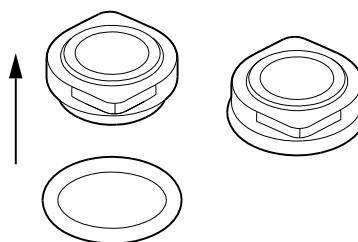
Монтаж уплотнительного кольца на неподвижной части торцевого уплотнения
